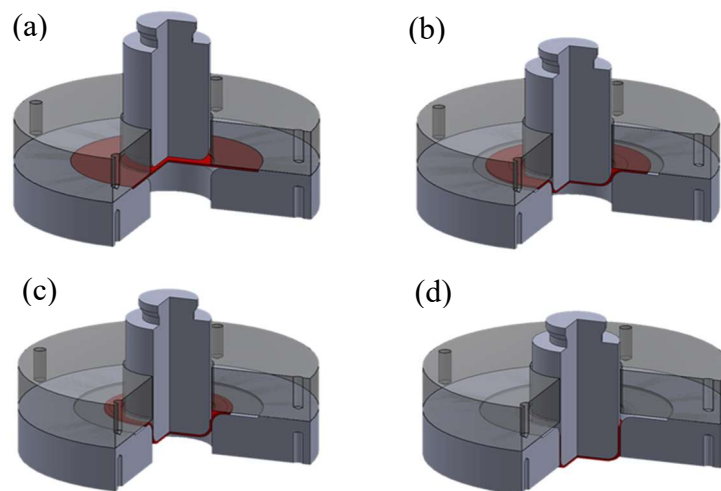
Principais estágios de uma operação de estampagem cilíndrica; (a) avanço do punção em direção à chapa, (b) final da 1ª fase de estampagem e início da 2ª, (c) 2º fase de estampagem e (d) final da operação. Adaptada de RODRIGUES e MARTINS (2010).
